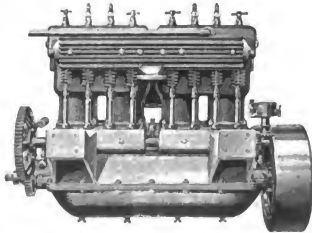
George Ville-Motor mit senkrechter Stromverteiler-Welle.
